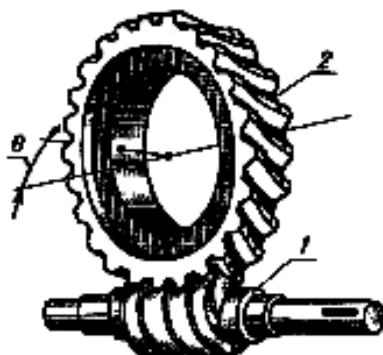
Червячная передача: 1 — червяк; 2 — венец червячного колеса.
